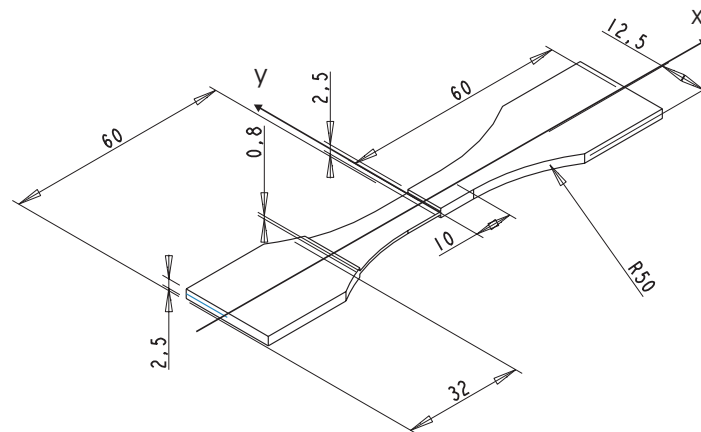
Géométrie de l'éprouvette (dimensions en mm)
